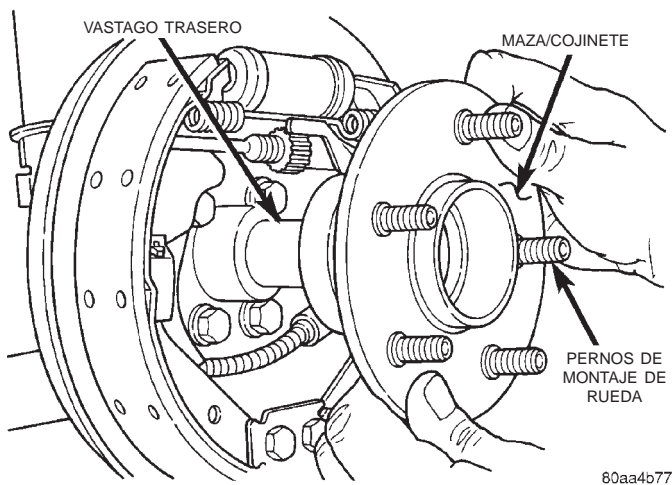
Desmontaje de maza/cojinete del vástago (Se muestran los frenos de tambor)
